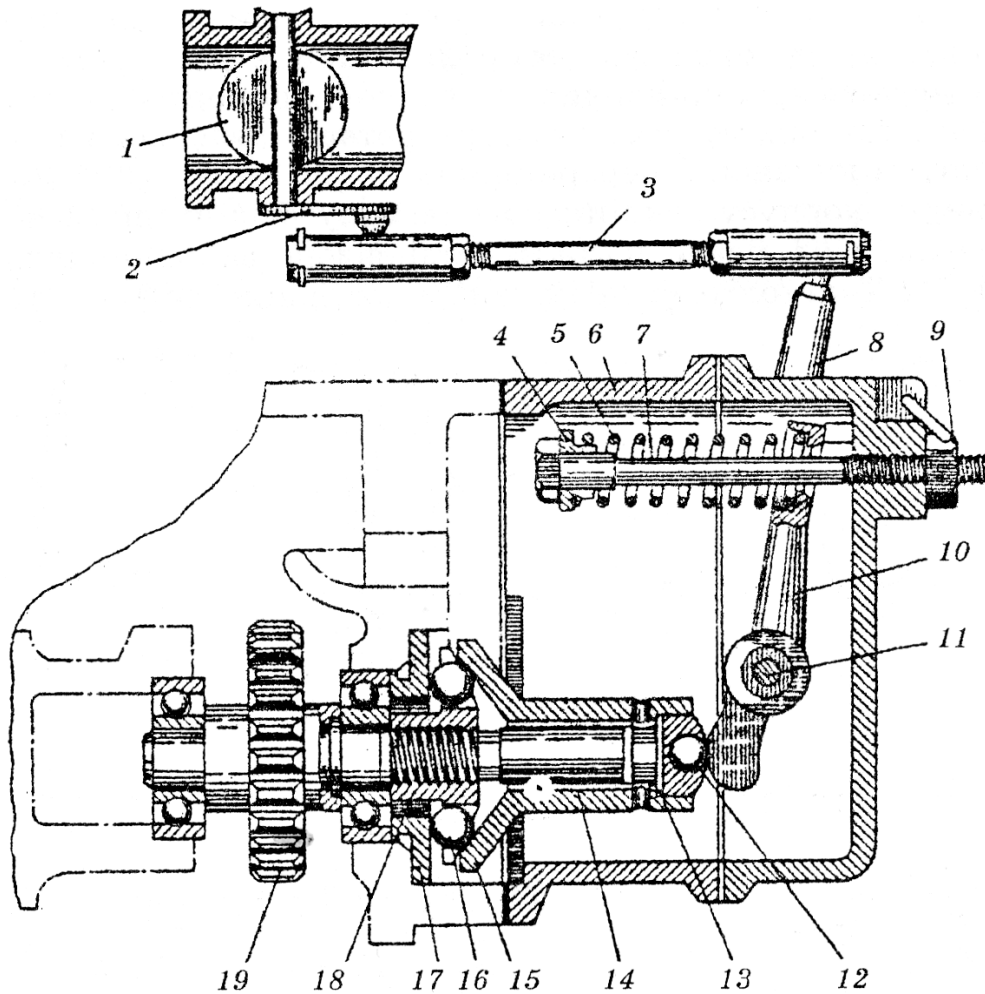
Однорежимний регулятор пускового двигуна:
